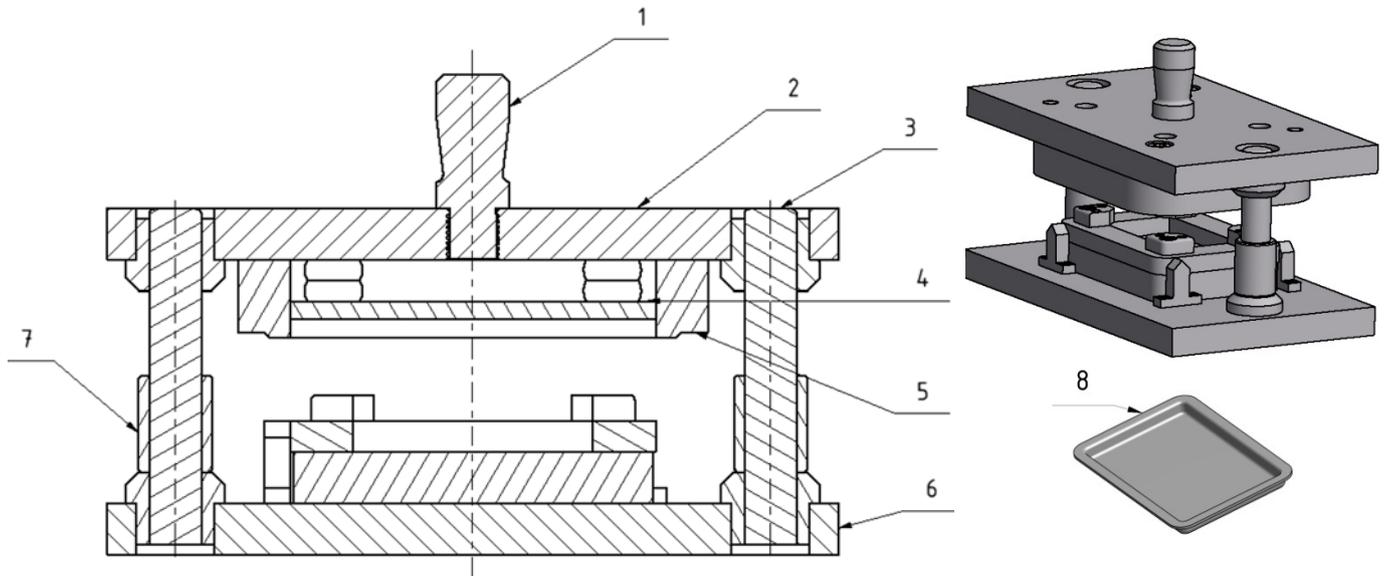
Folgeverbund-Werkzeug für eine Abdeckplatte
